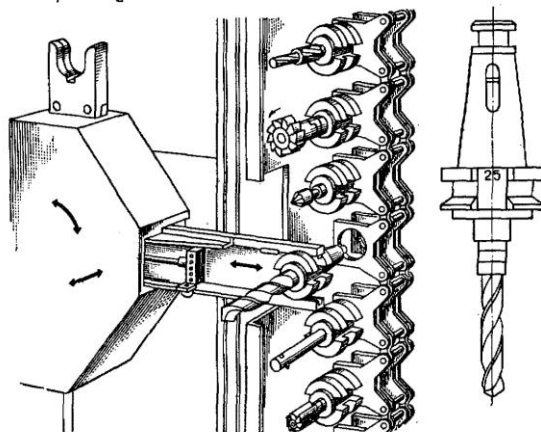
Механізм автоматичної заміни інструменту
